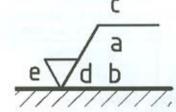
Základní značka struktury povrchu (rozměry platí pro výšku písma 3,5 mm)
